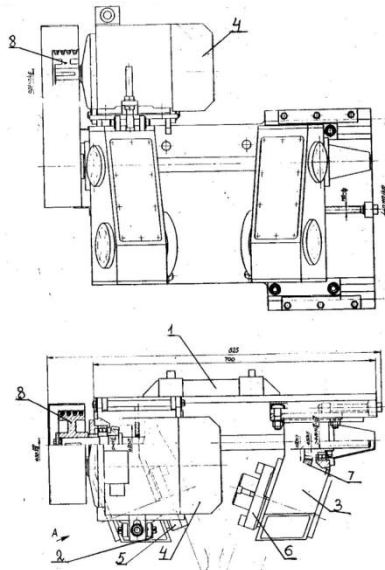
Принципиальная конструкция двухшпиндельного спецсуппорта к зубострогальному станку
